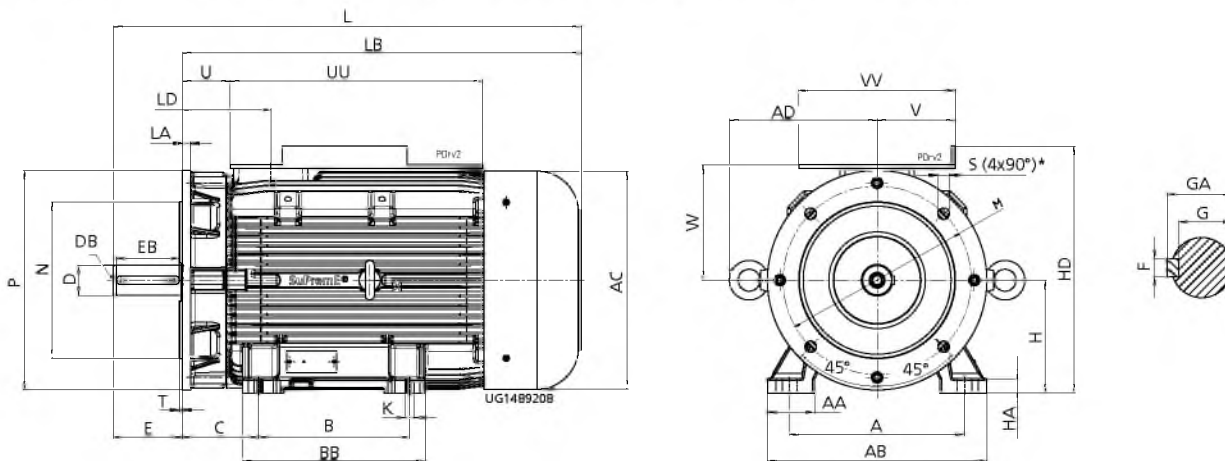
Двигатель с адаптером для PumpDrive 2 и фланцем FF с проходными отверстиями (V15,...)
